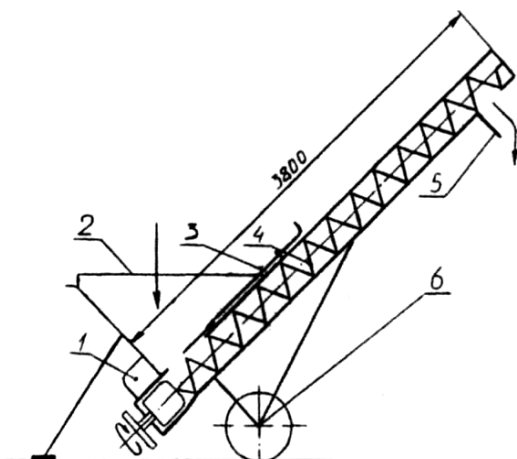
Пружинный зернопогрузчик производительностью 5 т/ч: 1 - заслонка; 2 - бункер; 3 - регулятор загрузки; 4 - пружина; 5 - лоток; 6 - колесо
